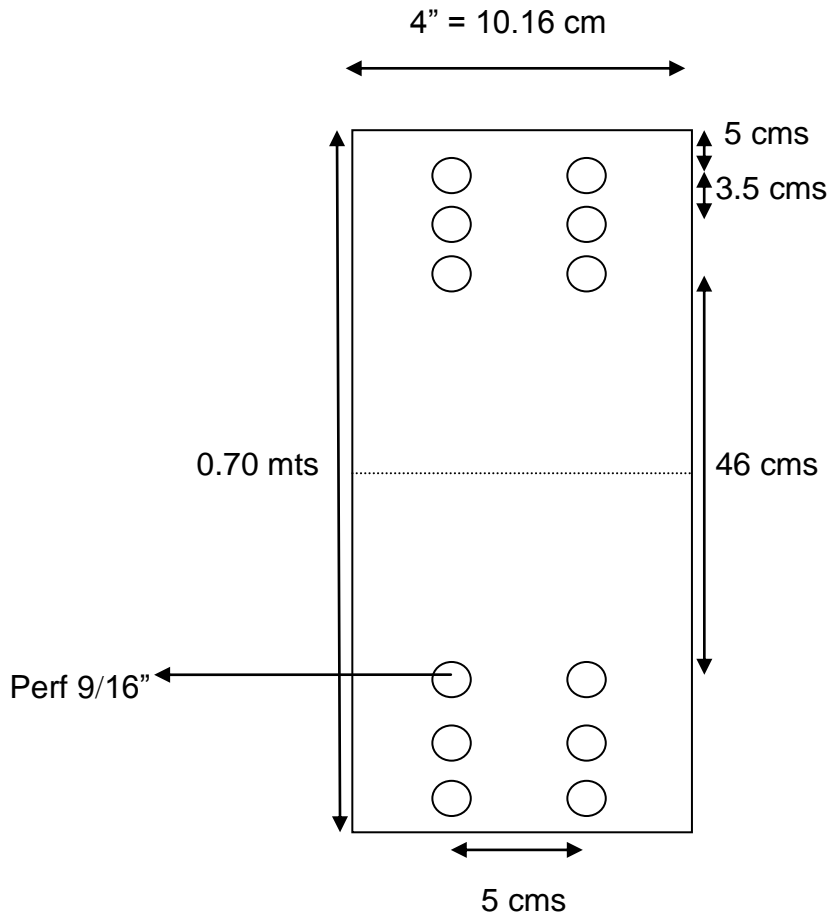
Geometría de la Platina Mordaza - Soldada.
